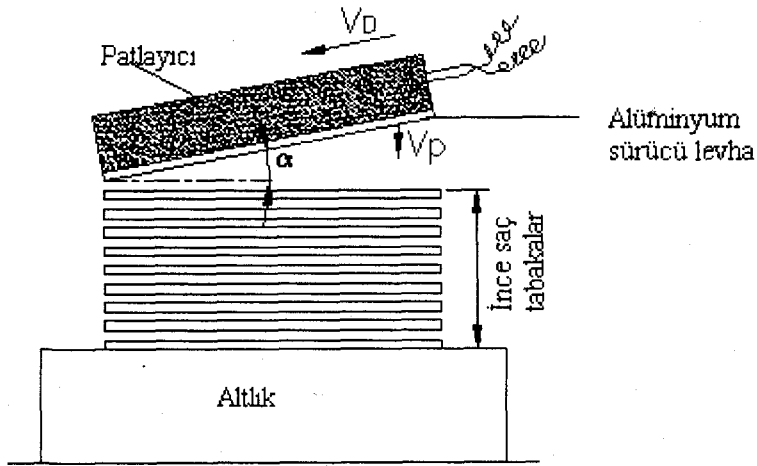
Patlama ile bindirme kaynağı [5]
